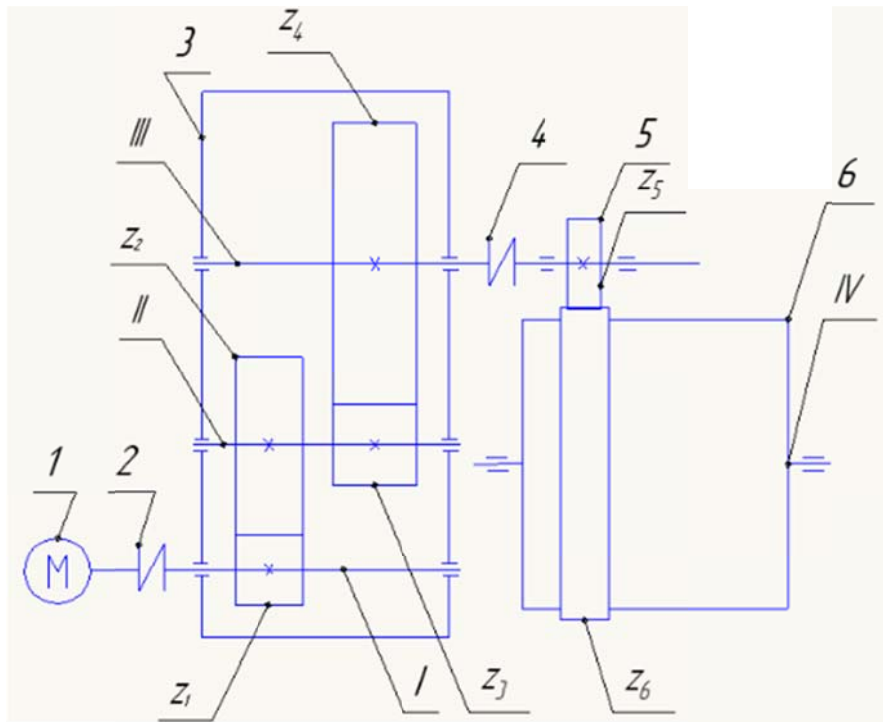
Кінематична схема приводу барабану: 1 – електродвигун; 2,4 – муфта; 3 – циліндричний двоступінчастий редуктор: I – швидкохідний вал редуктора, II – середній вал редуктора, III – тихохідний вал редуктора; 5 – відкрита циліндрична передача; 6 – барабан: IV – робочий вал барабанної сушарки
